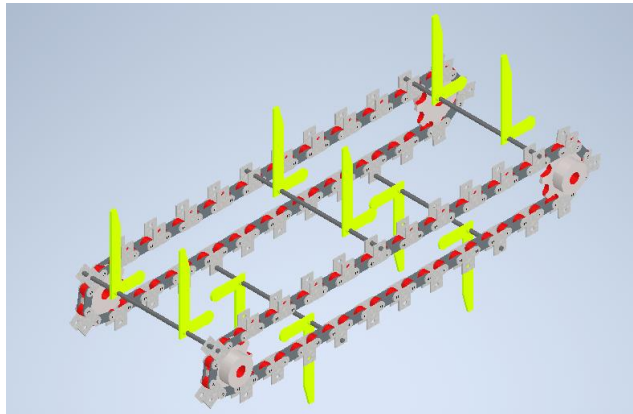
Esqueleto del elevador de listones formado con cadena tipo M.
